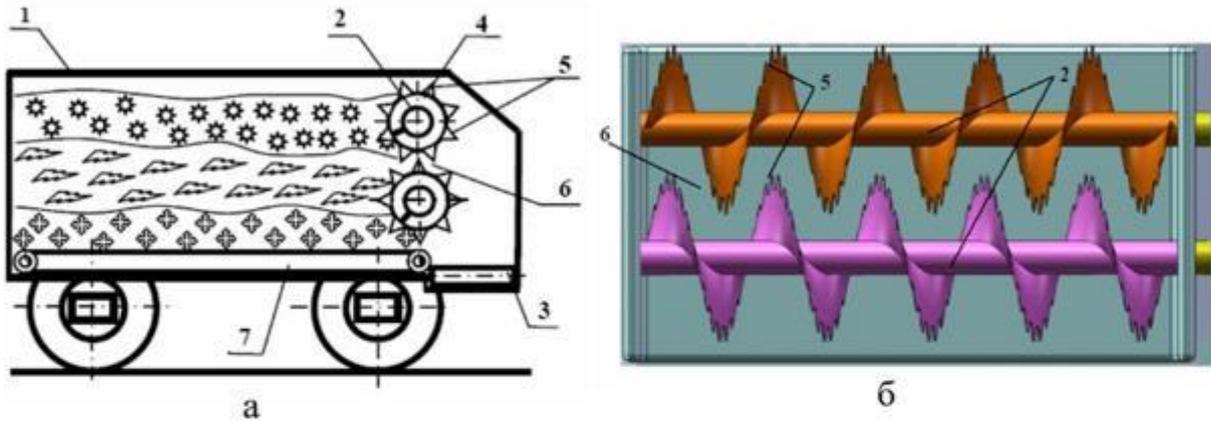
Конструктивно-технологічна схема змішувача-роздавача кормів (а) та шнековий робочий орган (б): 1 - бункер; 2 - подрібнювальний шнековий апарат; 3 – вивантажувальний транспортер; 4 - гвинтові поверхні; 5 - ножі; 6 - міжвитковий простір; 7 - поздовжній транспортер
